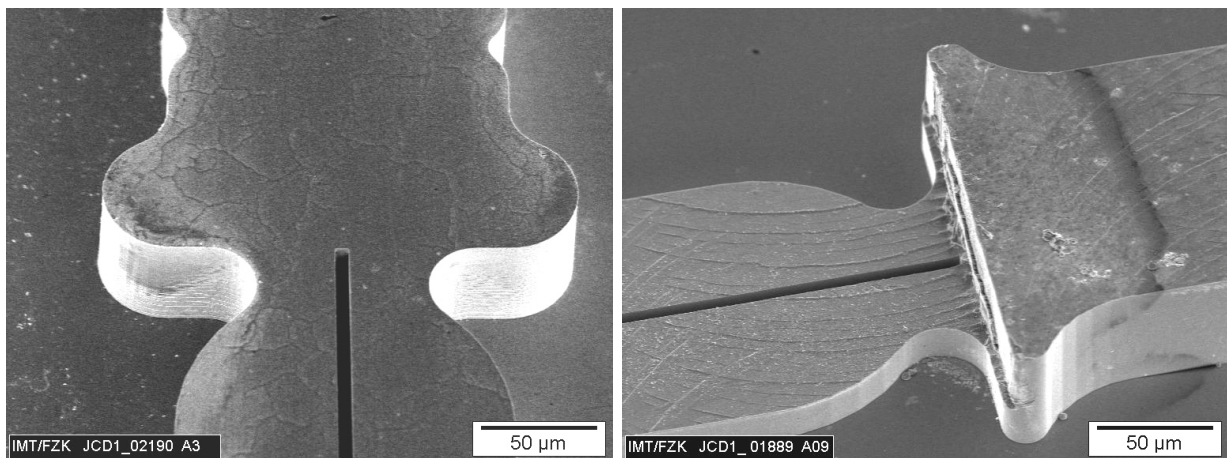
Formwerkzeug für Rippenwellenleiter mit Faserhaltестruktur. Links: ungestuftes Formwerkzeug. Rechts: gestuftes Formwerkzeug.
